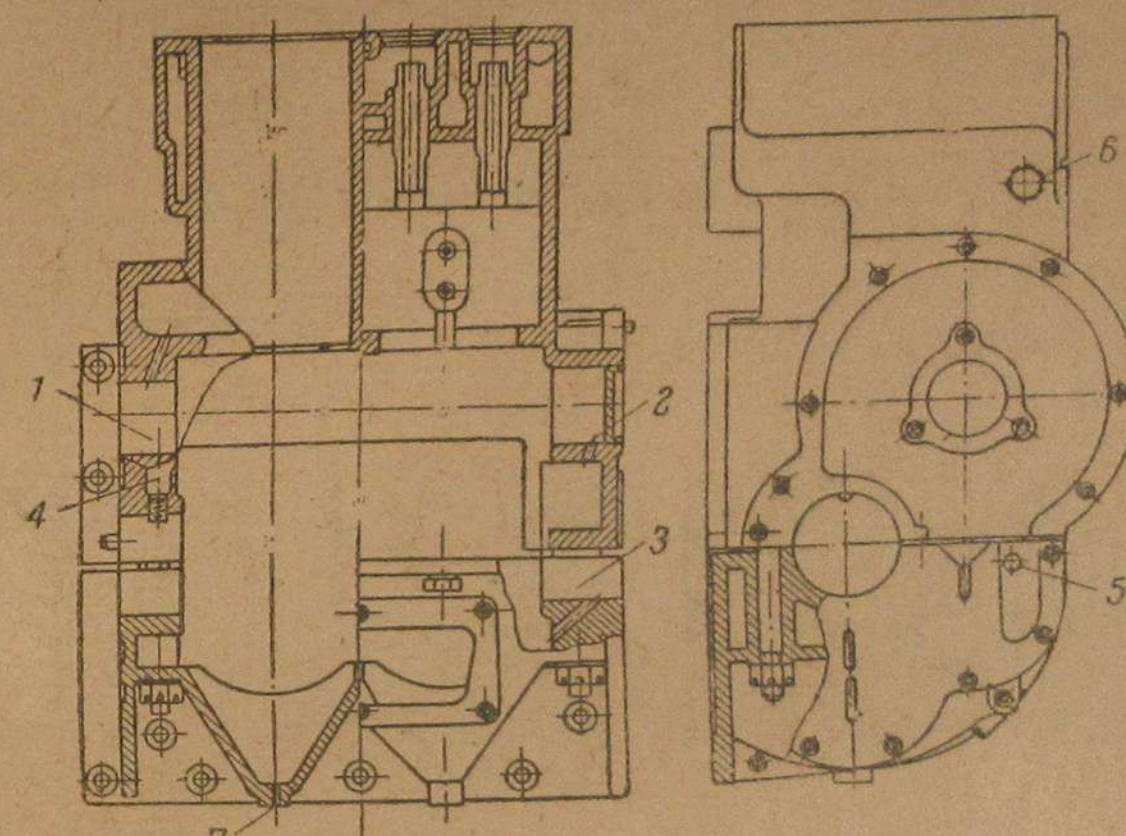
Разрез блок-картера двигателя В-20: 1 — передний подшипник для распределительного валика, 2 — отверстие для стока смазки в заднем подшипнике распределительного валика, 3 — гнездо заднего коренного подшипника, 4 — карман и отверстие для подвода смазки к коренному подшипнику, 5 — отверстие в картере для контроля уровня смазки, 6 — отверстие для установки сапуна, 7 — спускное отверстие картера
